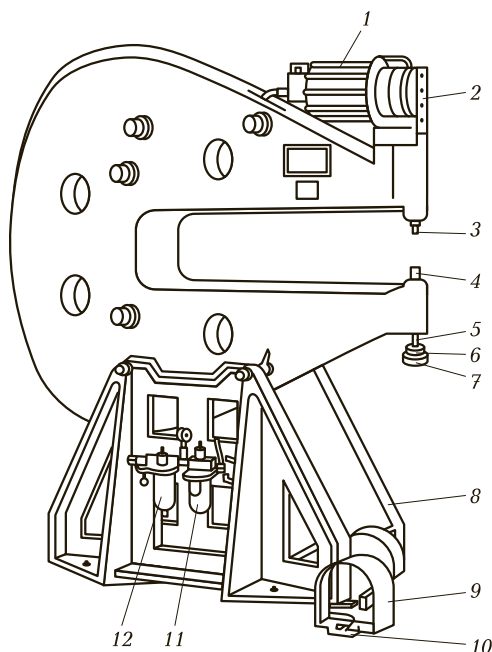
Пневморычажный стационарный пресс мод. КР204-М:
